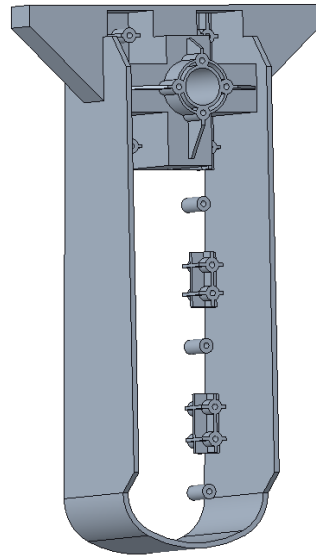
Columna media con torretas de atornillado columna/tapa.
